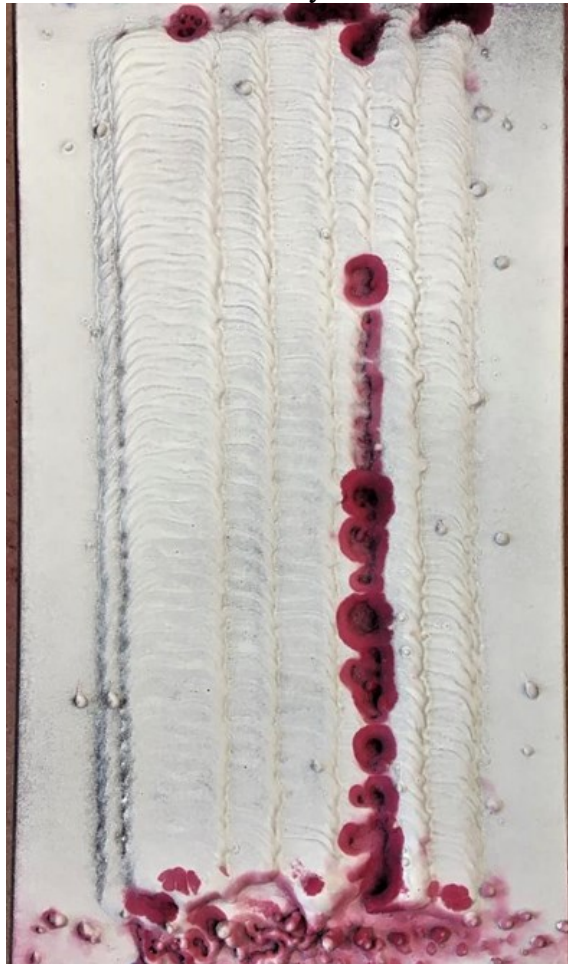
Duas camadas de revestimento com Stelloy 6 sob a chapa de CA6NM
